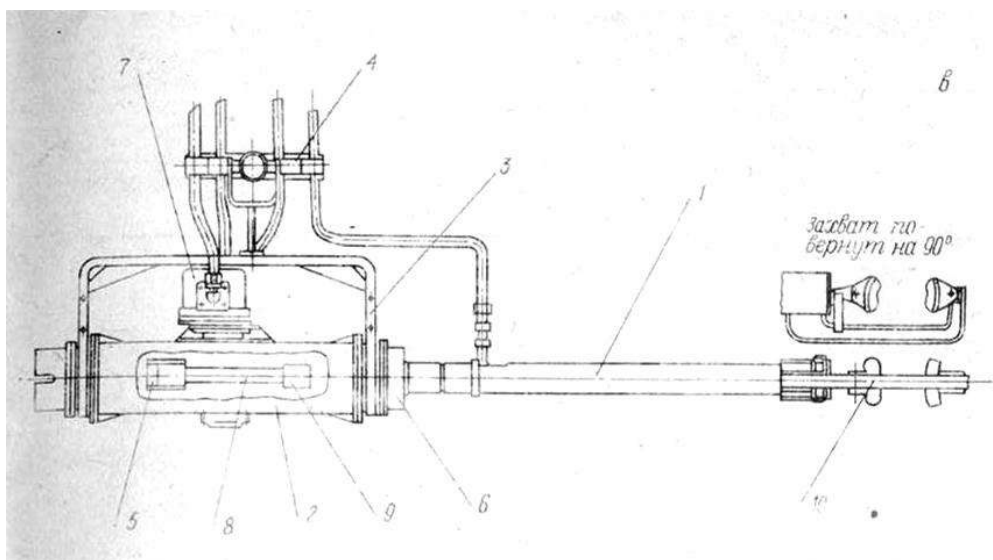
в. Встряхиватель для уборки плодов облепихи кулачковый:
